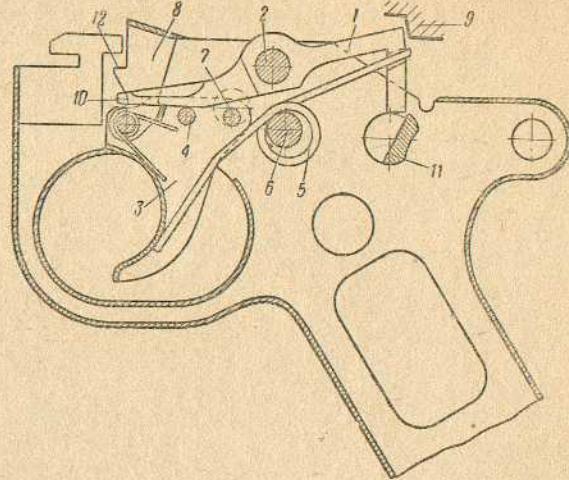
Схема положения частей спускового механизма при затворе, находящемся на боевом взводе: 1 — шептало; 2 — ось шептала; 3 — спусковой крючок; 4 — ось спускового крючка; 5 — пружина; 6 — ось пружины; 7 — штифт; 8 — хомутик; 9 — боевой взвод затвора; 10 — рожки переднего конца шептала; 11 — предохранитель; 12 — выступы хомутика
